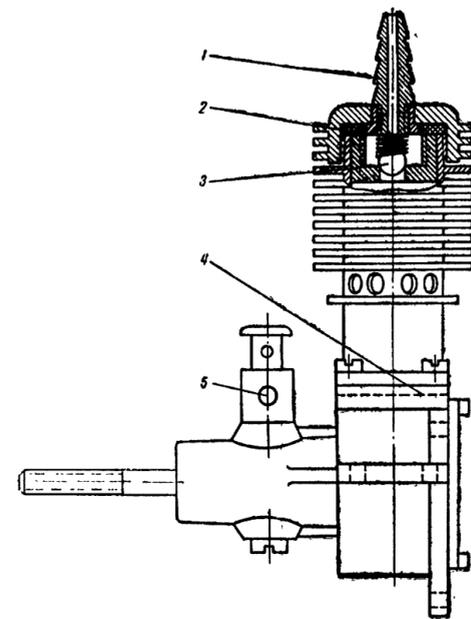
Компрессор, переоборудованный из двигателя К-16:
